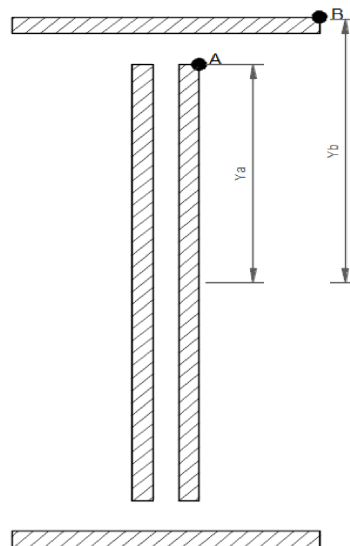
Filetes de soldadura - Puntos críticos
